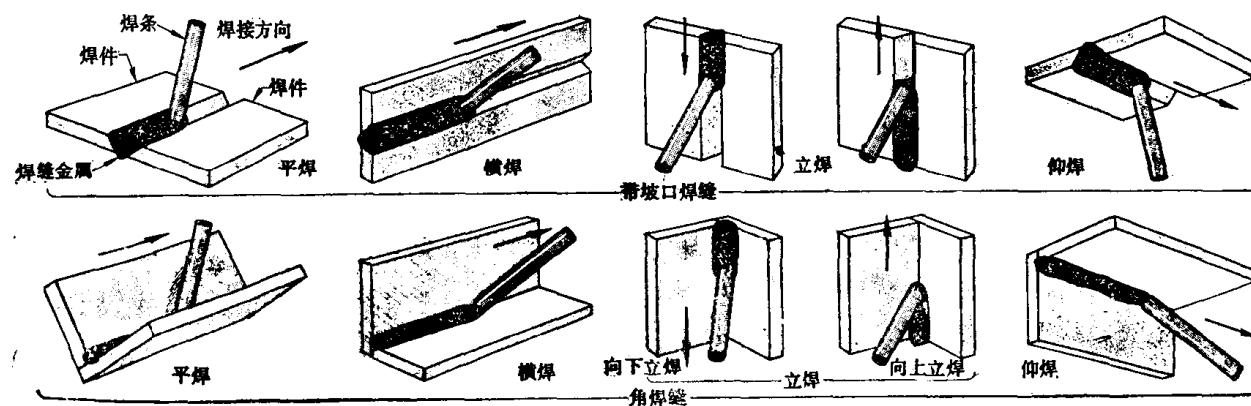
焊接带坡口焊缝(上排)和角焊缝(下排)常用的焊接位置
